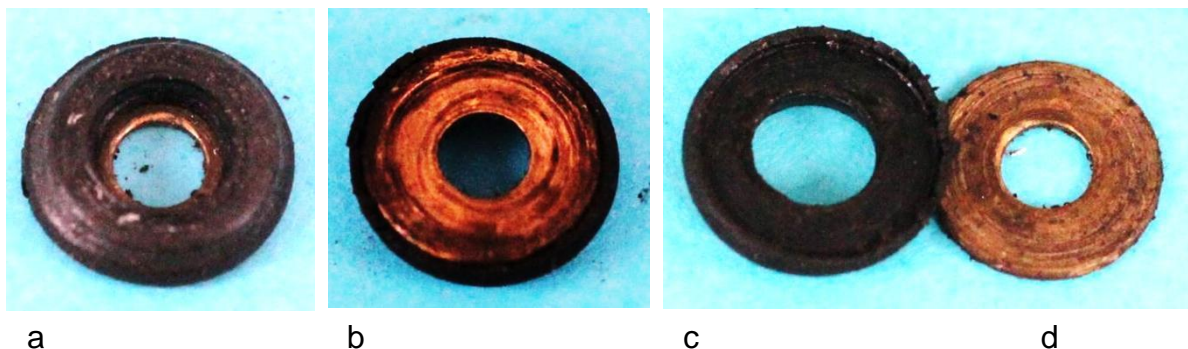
Einsatz im Boden: a) Isolierseite des Einsatzes, b) Kontaktseite des Einsatzes, c) Gummischeibe, d) Messingscheibe
